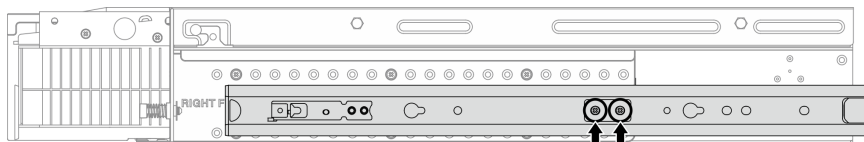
Deux vis pour la glissière interne de Kit de glissières ThinkEdge Friction 1 000 mm v2
